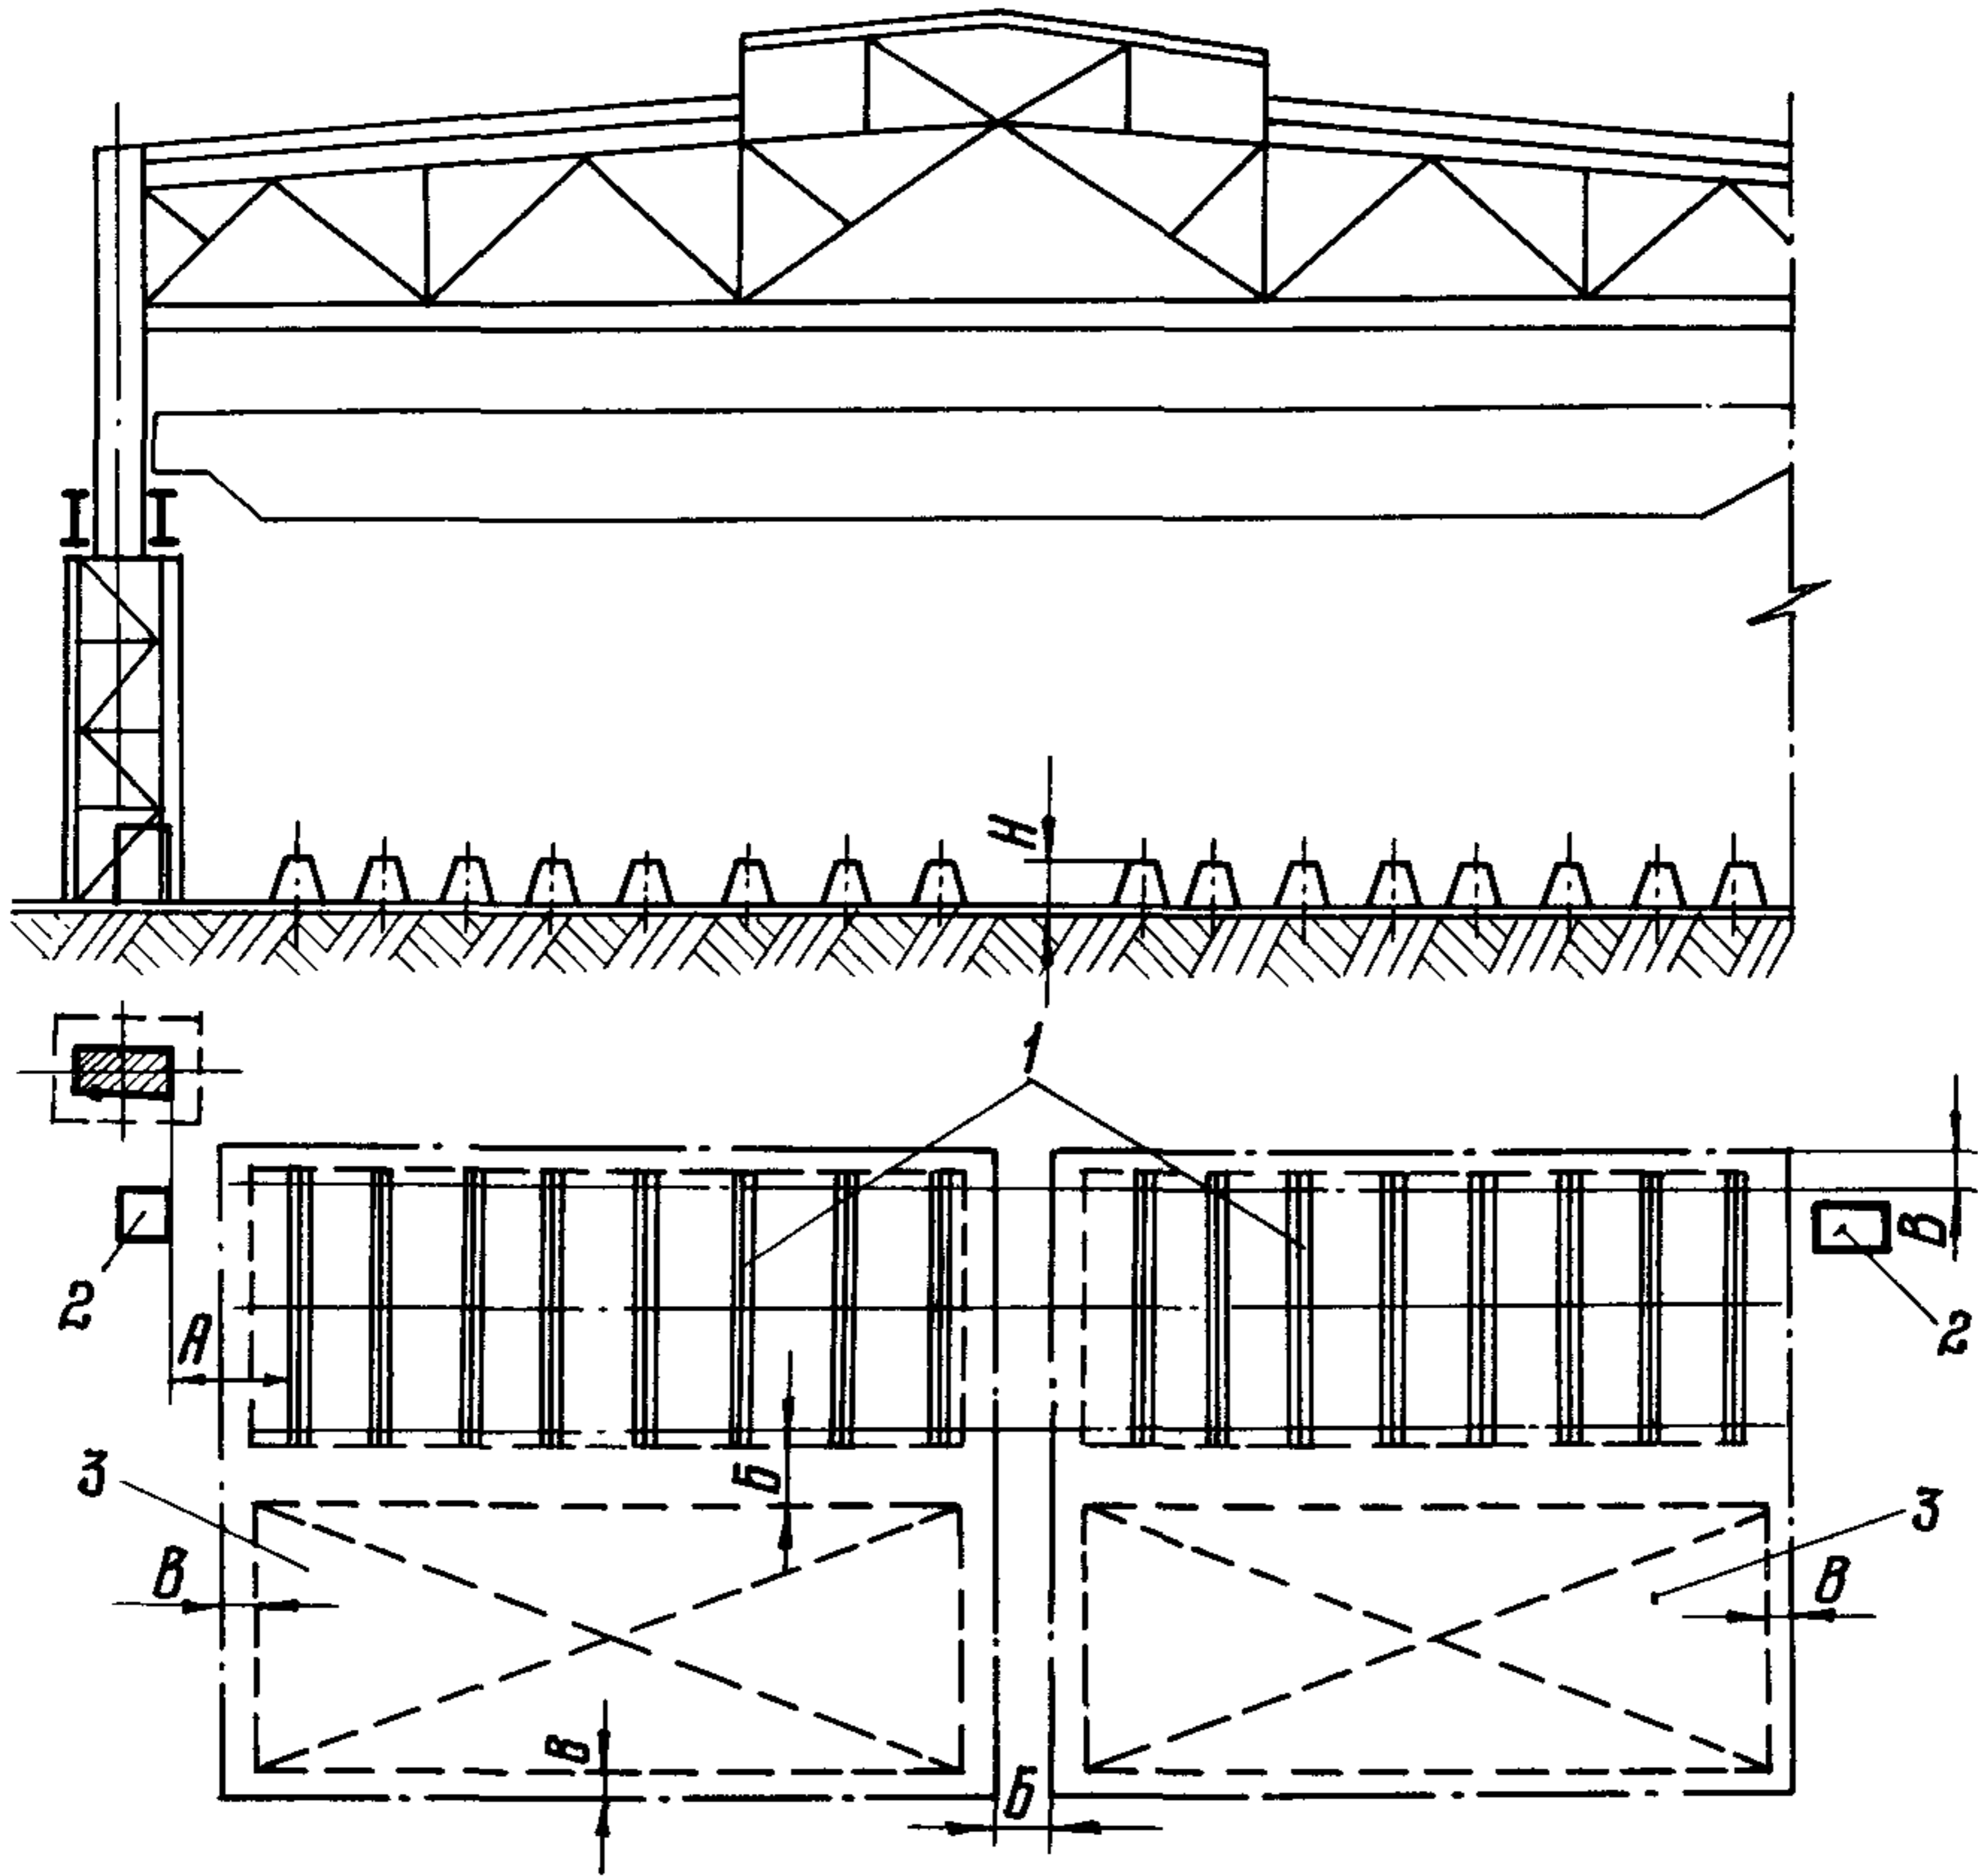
Размещение участка для сборки и сварки конструкций в поперечном пролете:
